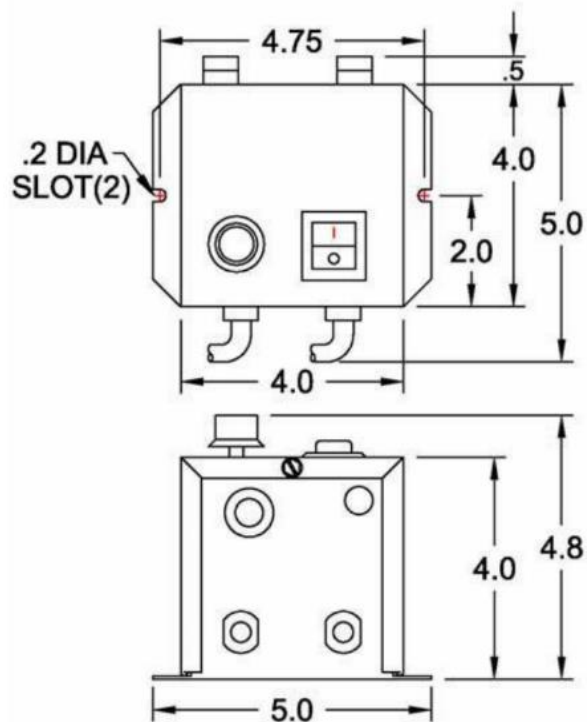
Dimensiones del controlador de vibraciones [29]
